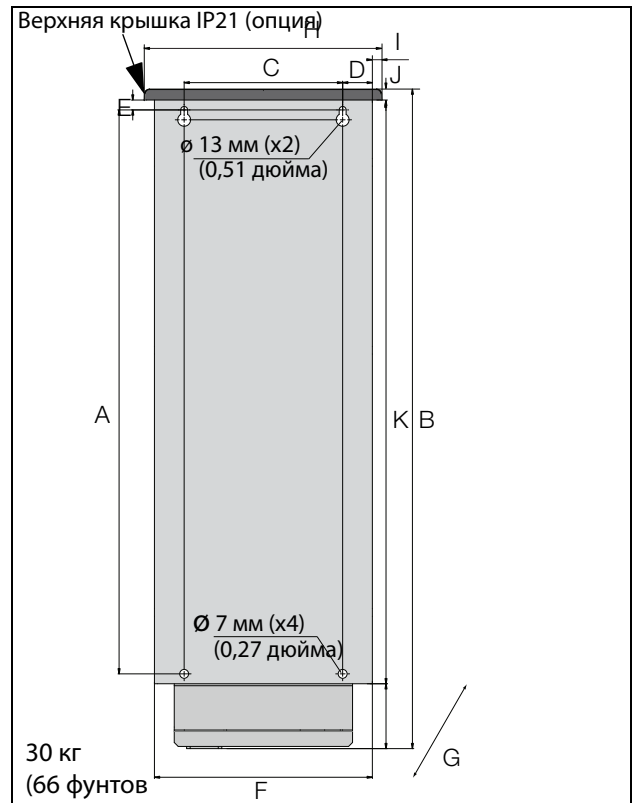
Устройство Emotron FDU моделей с 48-072 по 48-105 (размер корпуса D2), моделей с 69-033 по 69-058 (размер корпуса D2(69)), вид сзади.
